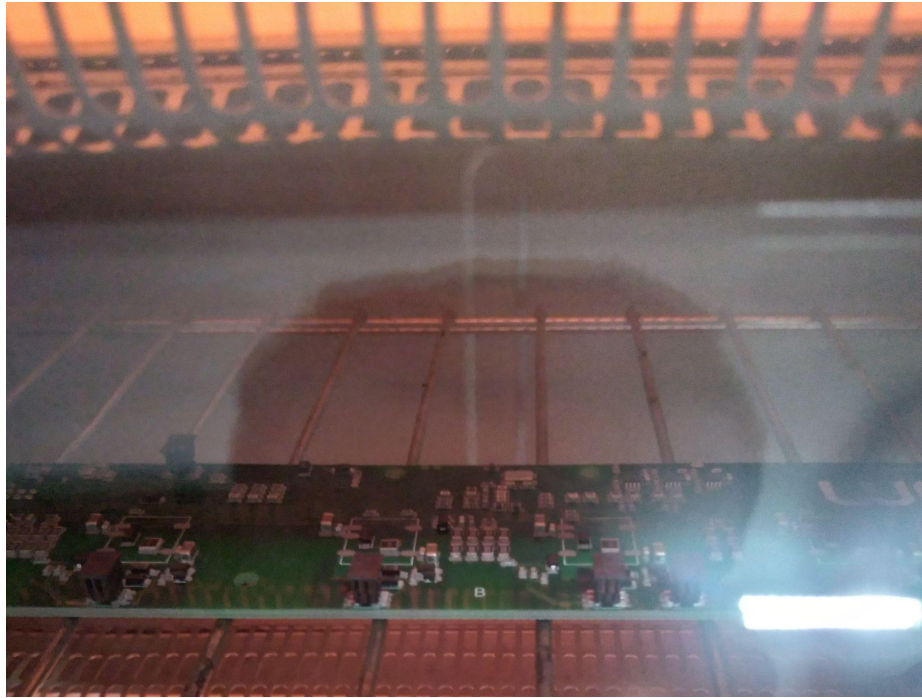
Proceso de ensamblaje de la placa de control (Controller Board)
